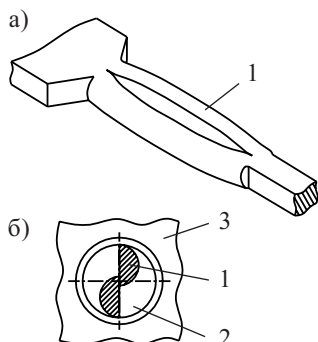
Контактный штырь круглого сечения: а — до запрессовки; б — после запрессовки
